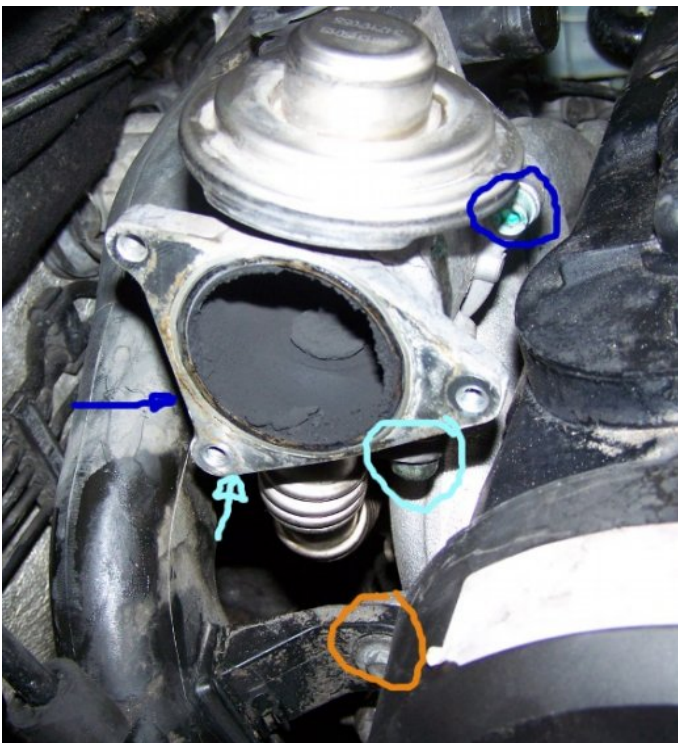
Ausbau des AGR-Ventils, Schrauben und Werkzeug
